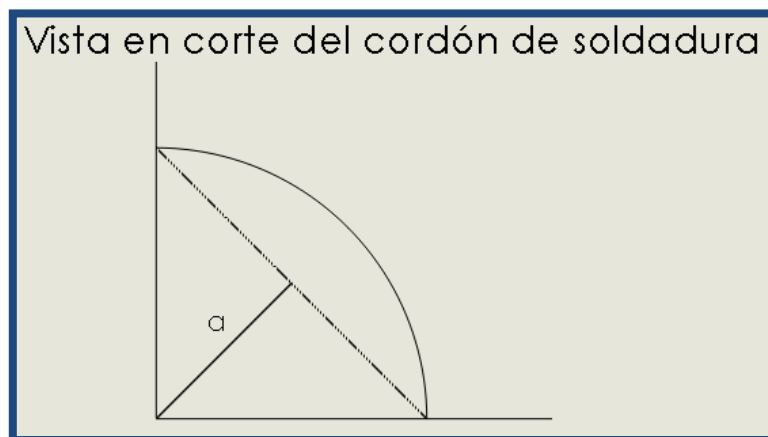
Vista en corte del cordón de soldadura.
